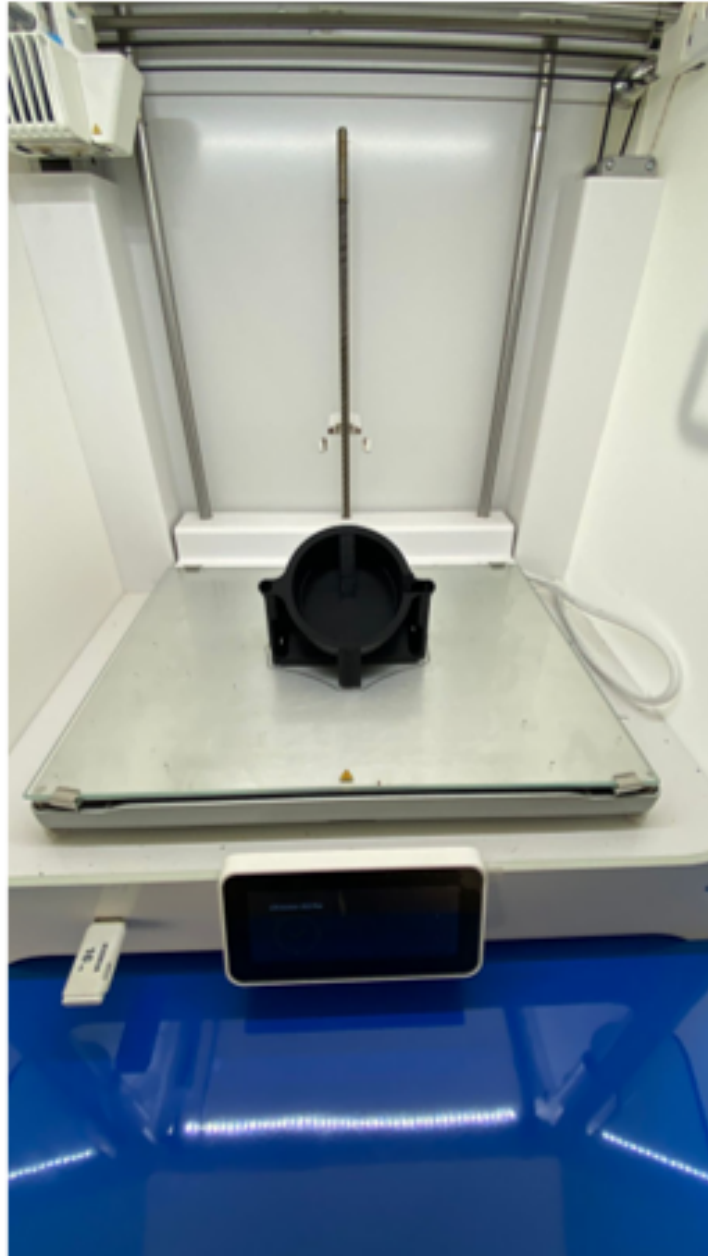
Impresión 3D de soporte de actuador blando. Elaborado por autores.
